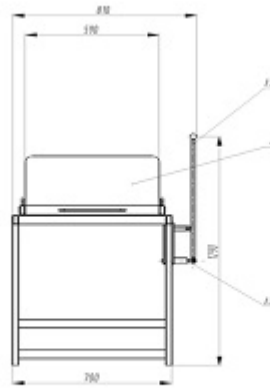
Модель поворотного стола для проведения тилт-теста (вид сбоку)
